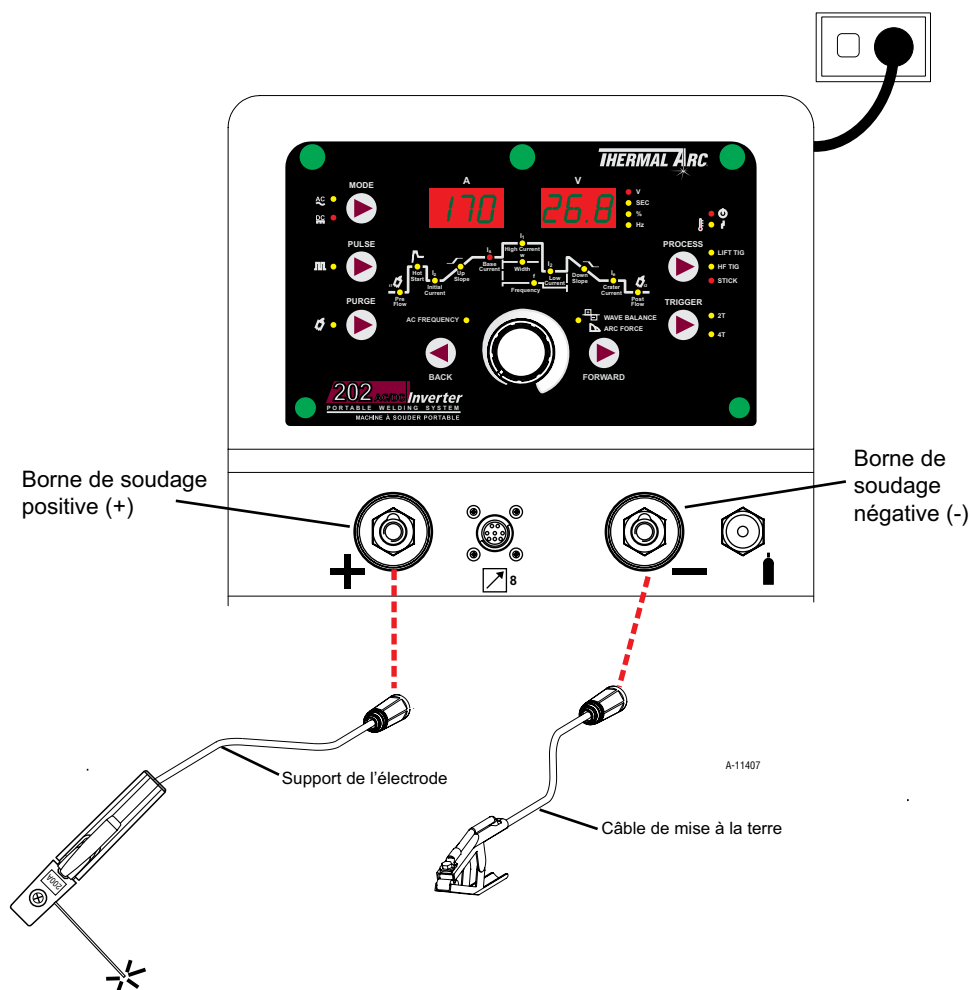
Configuration pour le soudage à l'arc manuel.
